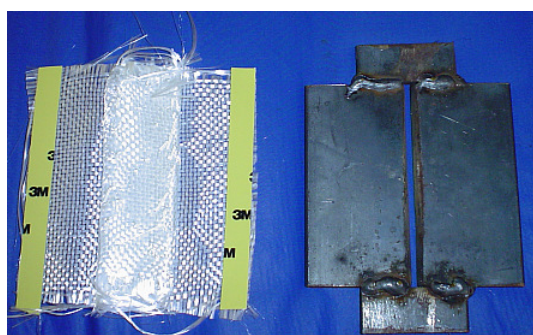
Suporte de solda e chapa antes da montagem do conjunto.
